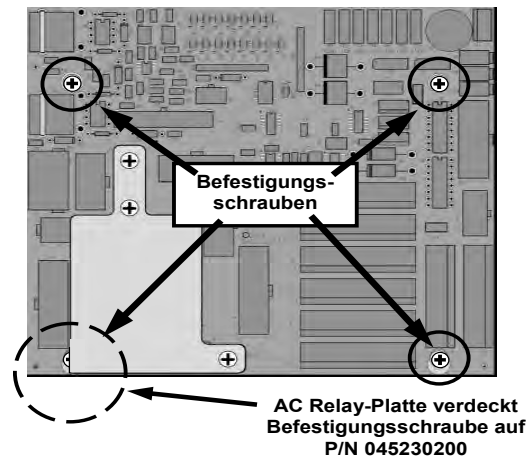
Befestigungsschrauben der Relais-Platine
